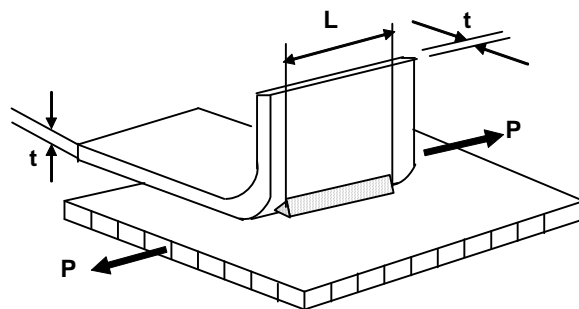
Soldadura a tope acampanada en bisel cargada longitudinalmente.
